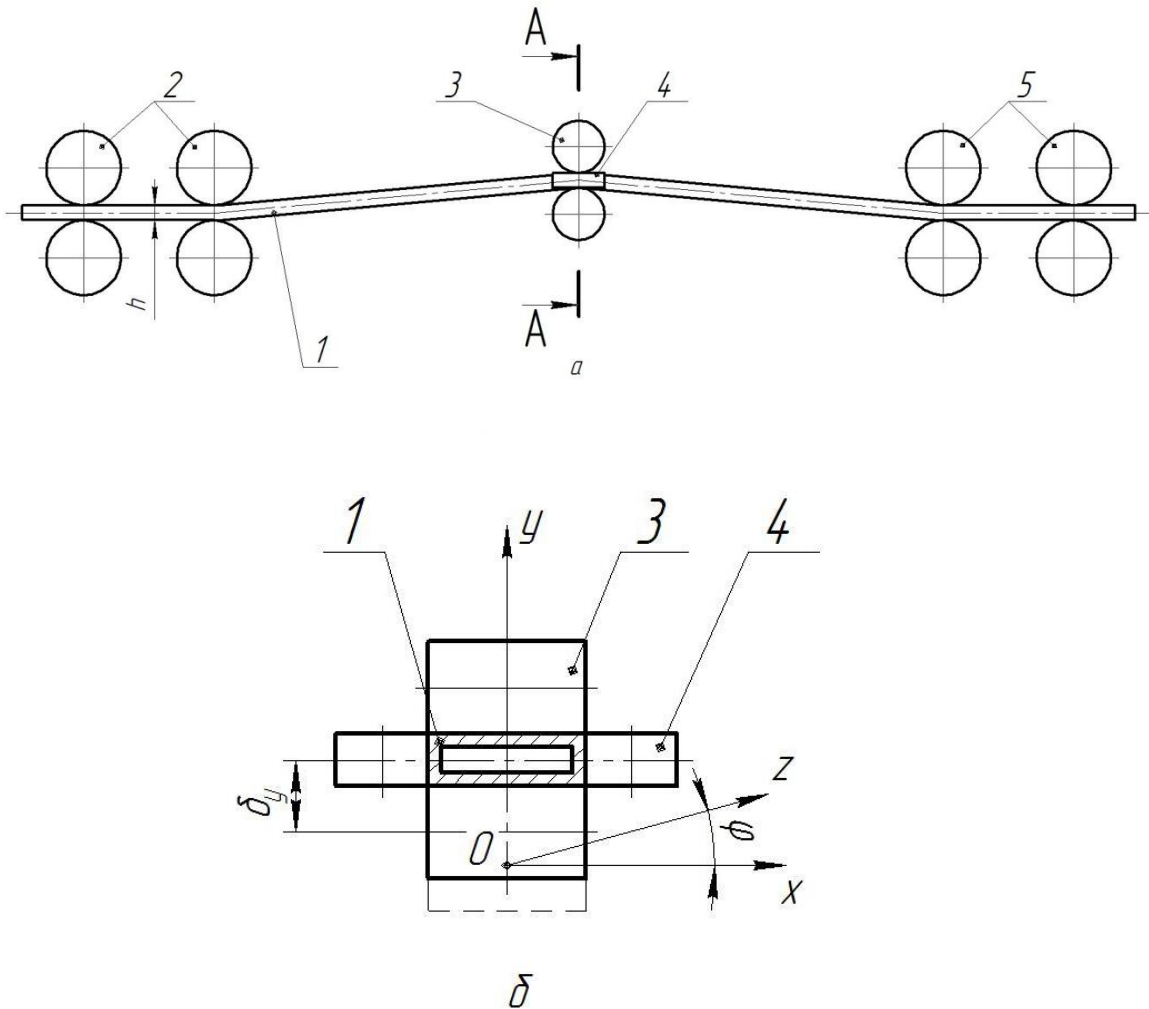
Схема изгиба заготовки обоймой роликов, совершающих движение по замкнутой траектории
